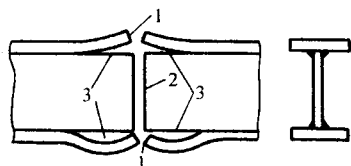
工字梁对接接头的焊接顺序
